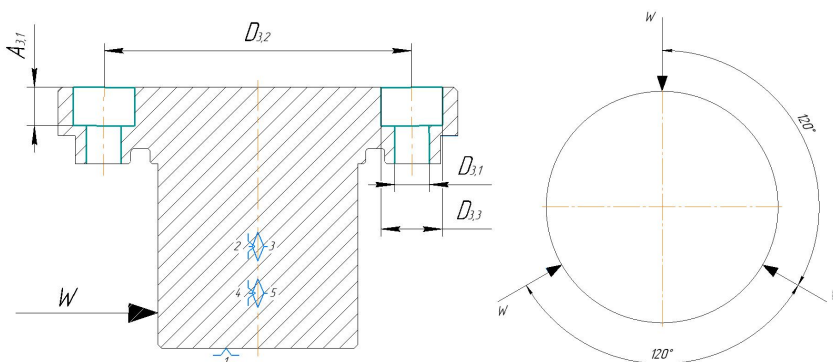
Принципиальная схема зажима заготовки в приспособлении с указанием мест приложения силы зажима.
